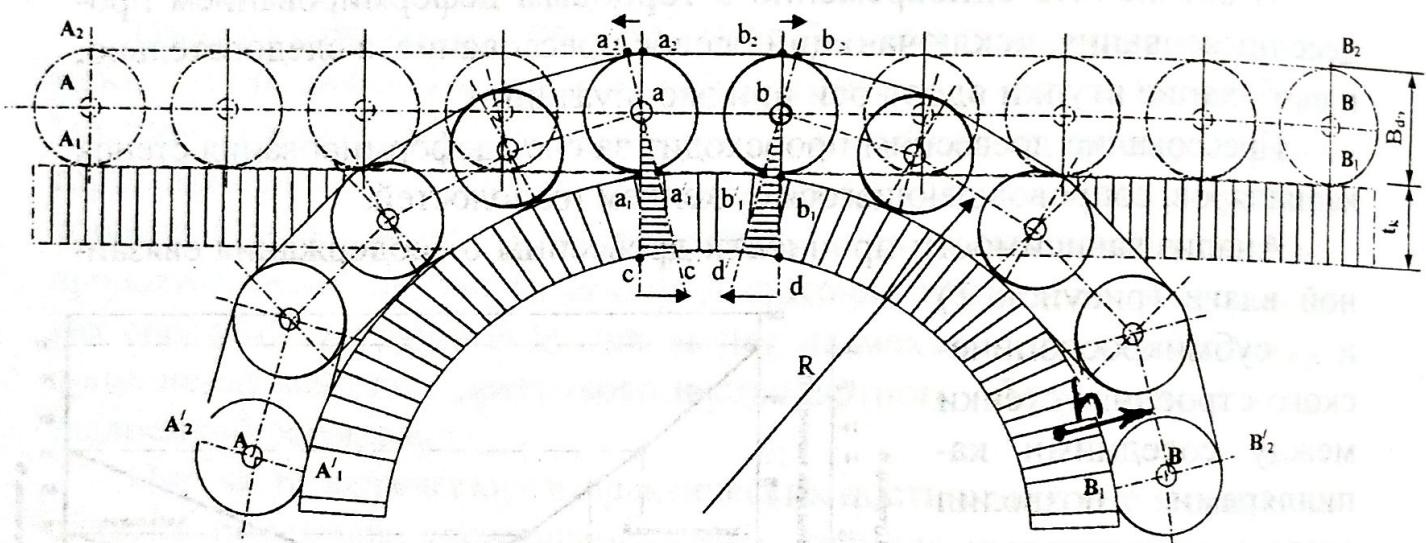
Схема торцевого деформирования древесной карточки 1 дискретным элементом 2 с одновременным прессованием
